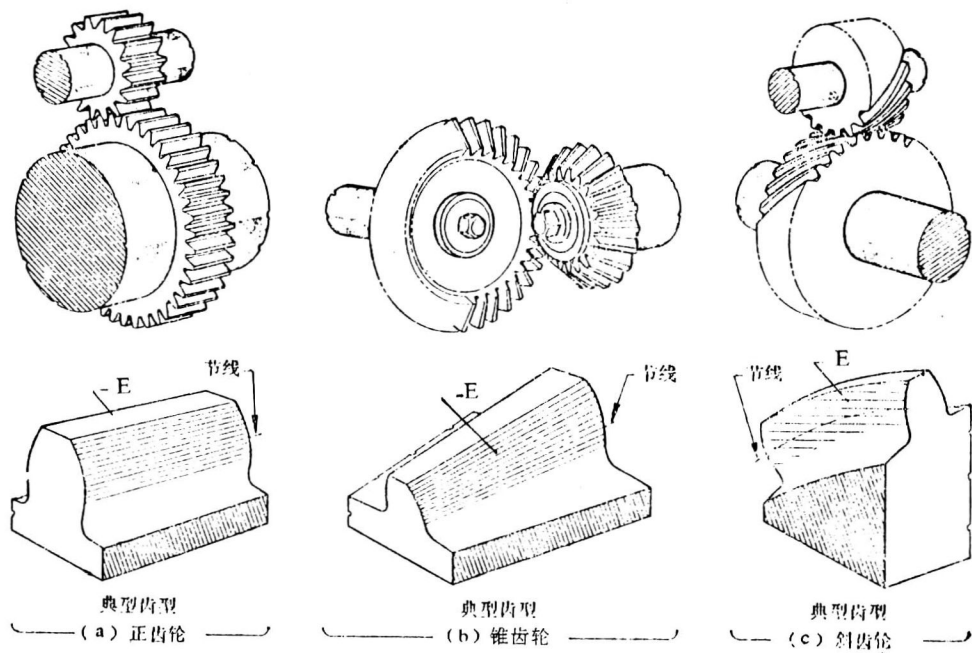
正齿轮、锥齿轮和斜齿轮上的轮齿在啮合时的接触线 (E)
